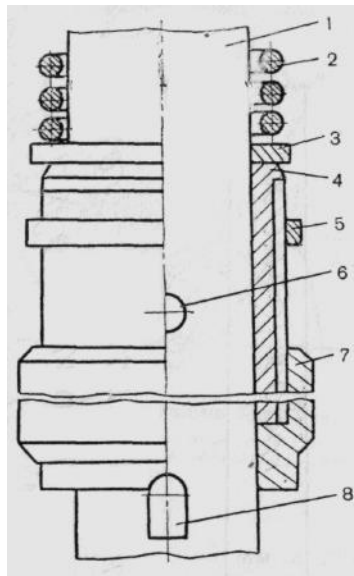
Пристрій для регулювання глибини ходу сошників:
